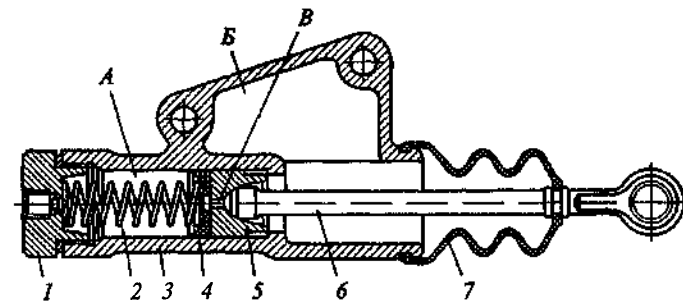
Главный цилиндр привода сцепления грузового автомобиля КамАЗ:
